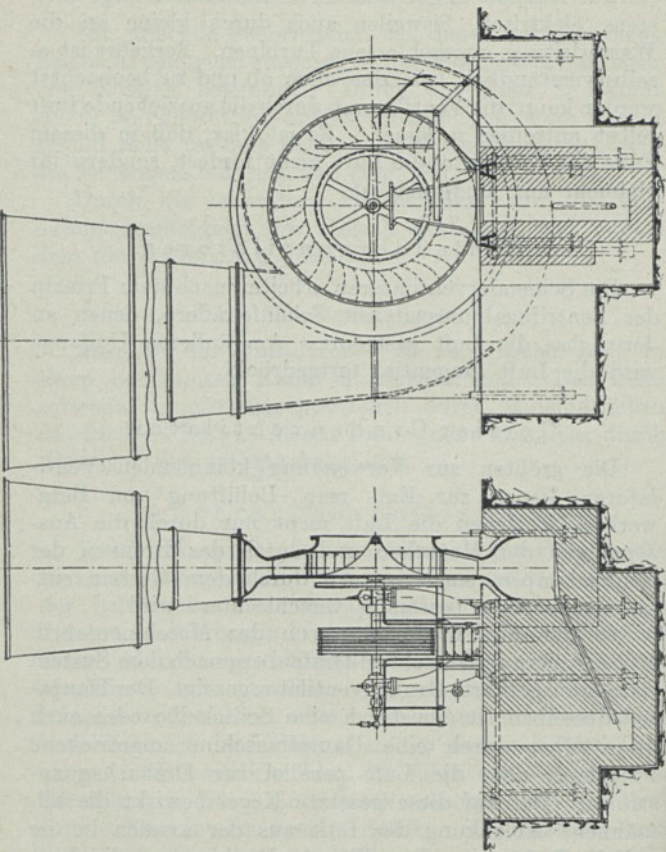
Geisler Grubventilator. Maschinenzollern Hohenzollern Düsseldorf-Grafenberg.
